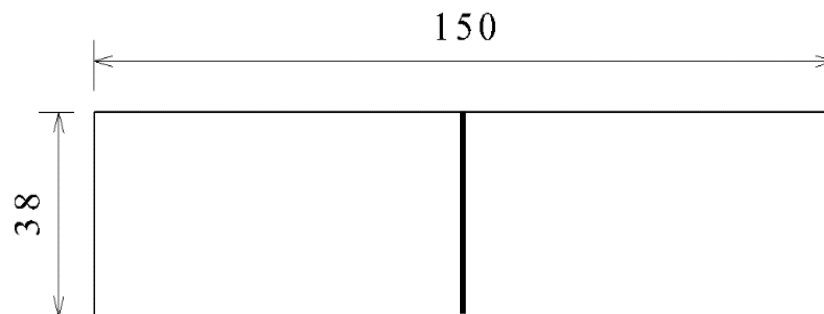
Dimensões dos provetes para o ensaio de dobragem.
